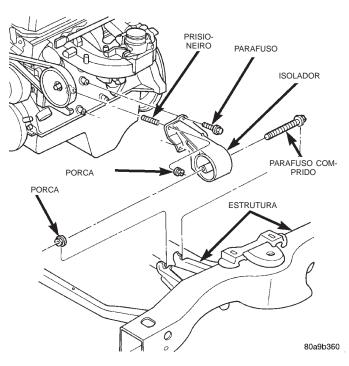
Conjunto Dianteiro Esquerdo de Montagem do Motor
